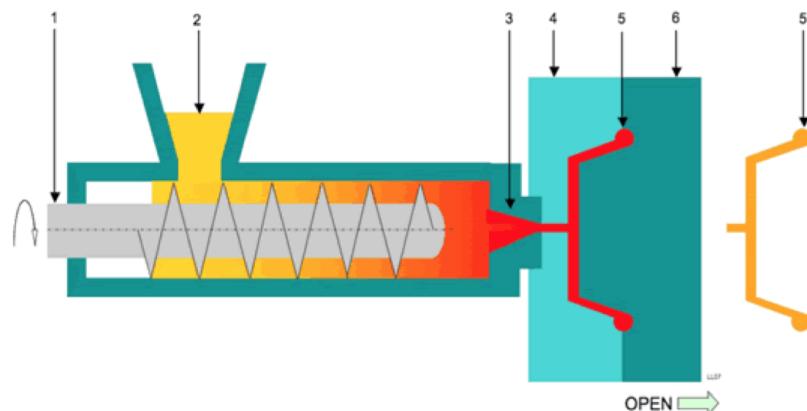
Procédé d'injection plastique (1-vis d'injection ; 2-granulés ; 3-buse d'injection ; 4- moule fixe ; 5-pièce injectée ; 6- moule mobile)
